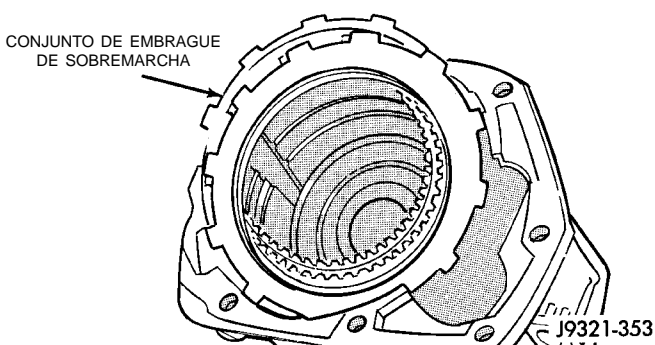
Desmontaje del conjunto de embrague de sobremarcha
